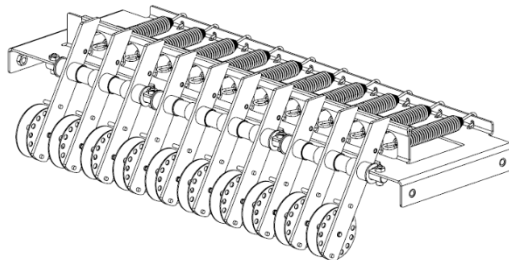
, Brake/Encoder Assembly (rem/encoderunit)
